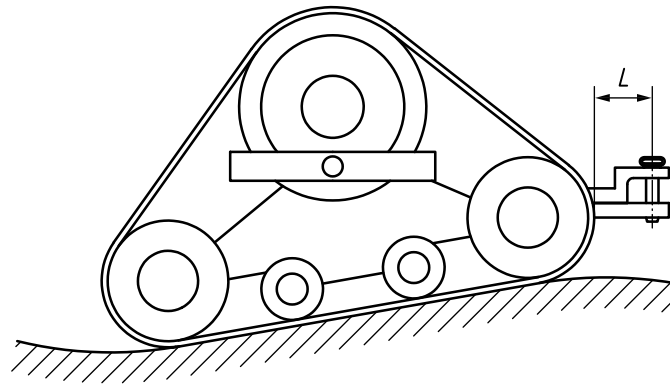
Emplacement de la dimension L — Tracteurs à chenilles
